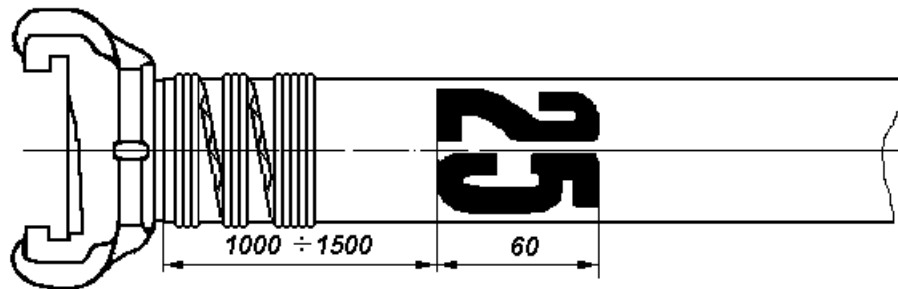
Дополнительная маркировка рукава на рукавной базе
